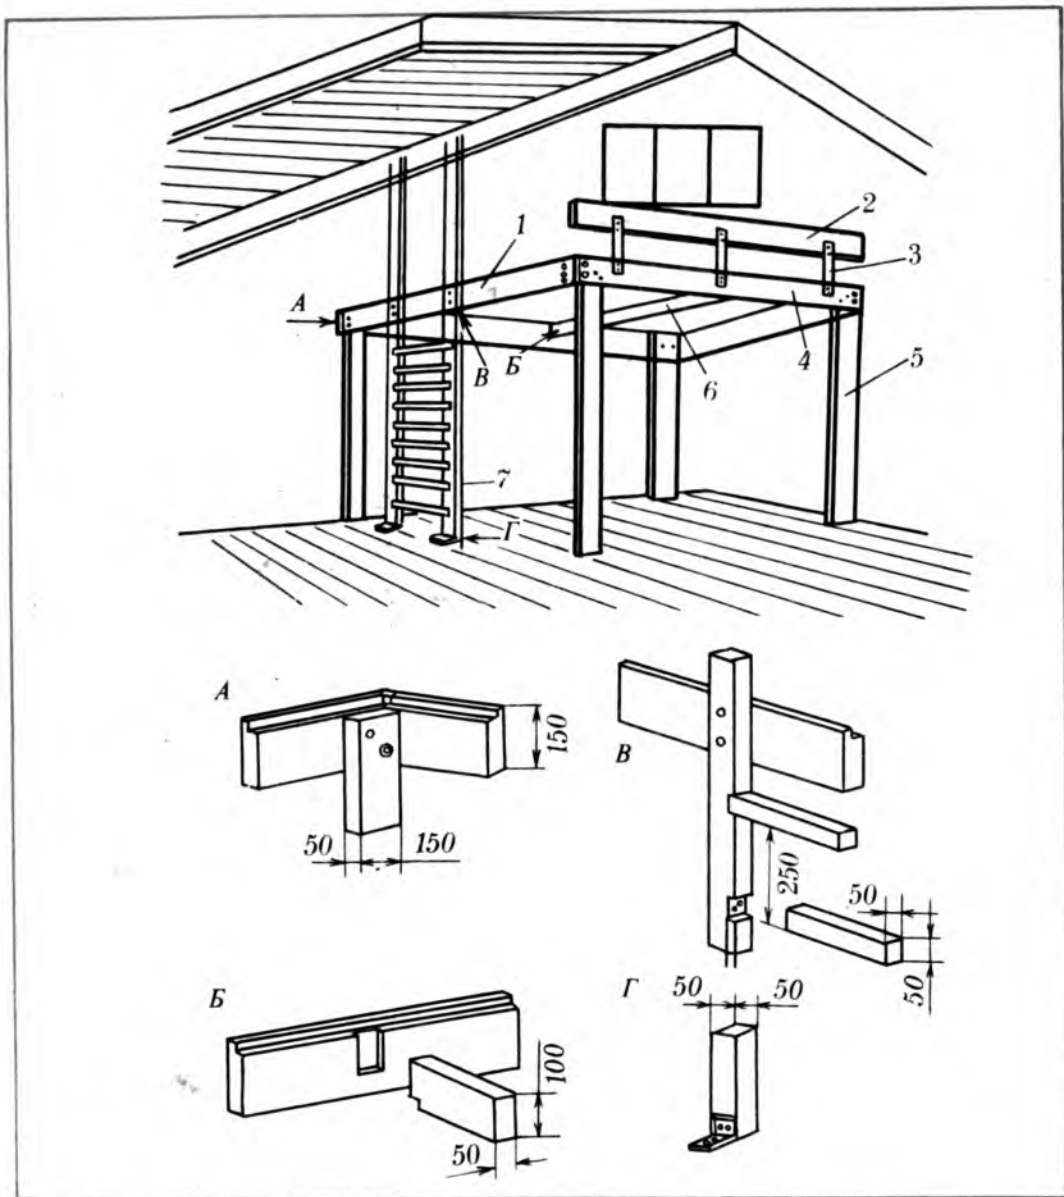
Кровать под потолком: 1 — продольная царга; 2 — парапет; 3 — стойка парапета; 4 — поперечная царга; 5 — стойка кровати; 6 — средняя царга; 7 — стойка лестницы
